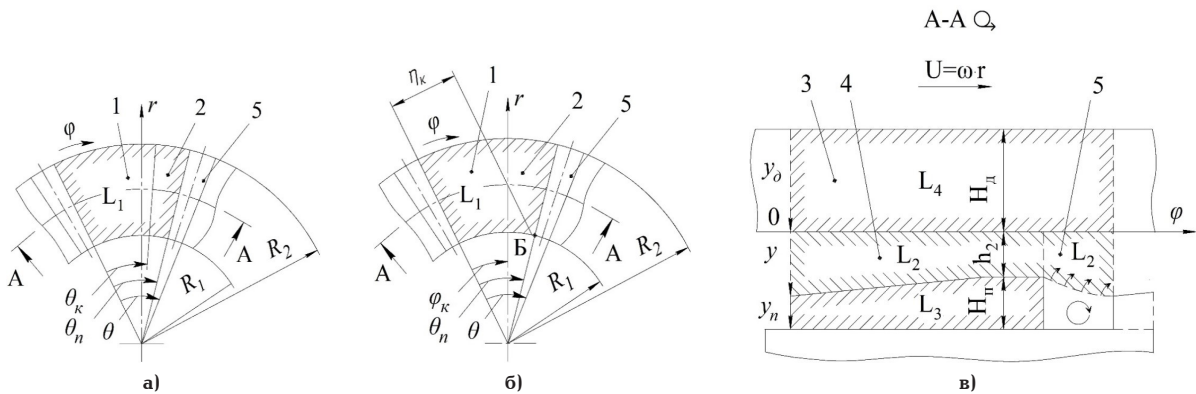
Расчетная схема упорного подшипника скольжения: а — профиль подушки с винтовой поверхностью; б — профиль подушки с параллельным МПК скосом; в — разрез по А-А вдоль среднего радиуса; 1, 2 — клиновая и плоская части подушки; 3 — упорный диск; 4, 5 — смазочный и пограничный слой; $\theta_\kappa, \theta_n, \theta$ — угловые протяженности клина, подушки и элемента периодичности; H_n, H_κ — толщины подушки и диска
